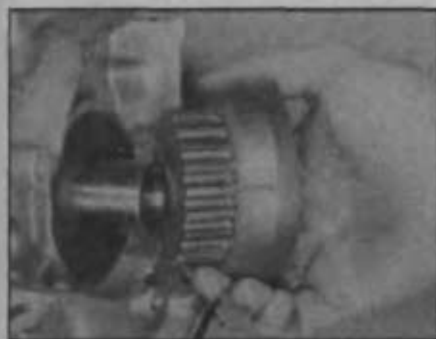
Снятие шкива зубчатого ремня с коленчатого вала
